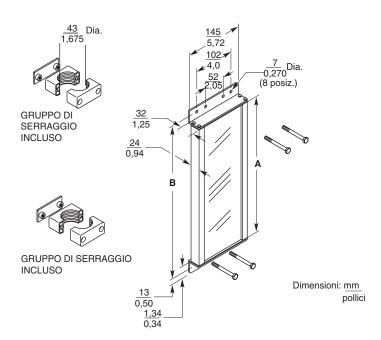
Dimensioni degli specchi (Vedere Tabella 42 per le dimensioni A e B)
